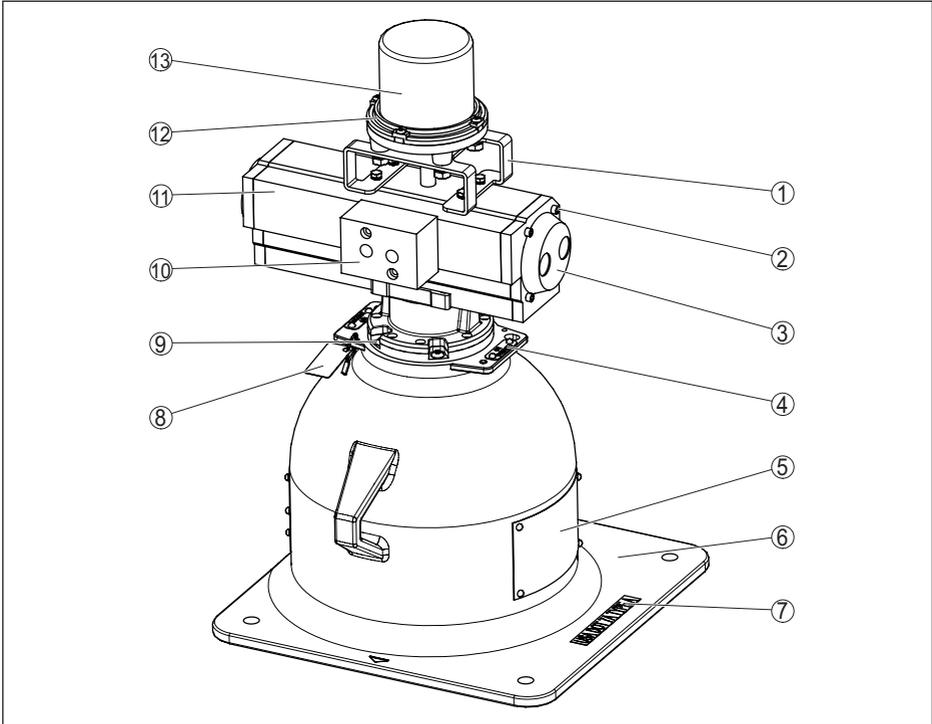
Werkstoffe VEGASOURCE 83 - Ausführung B
